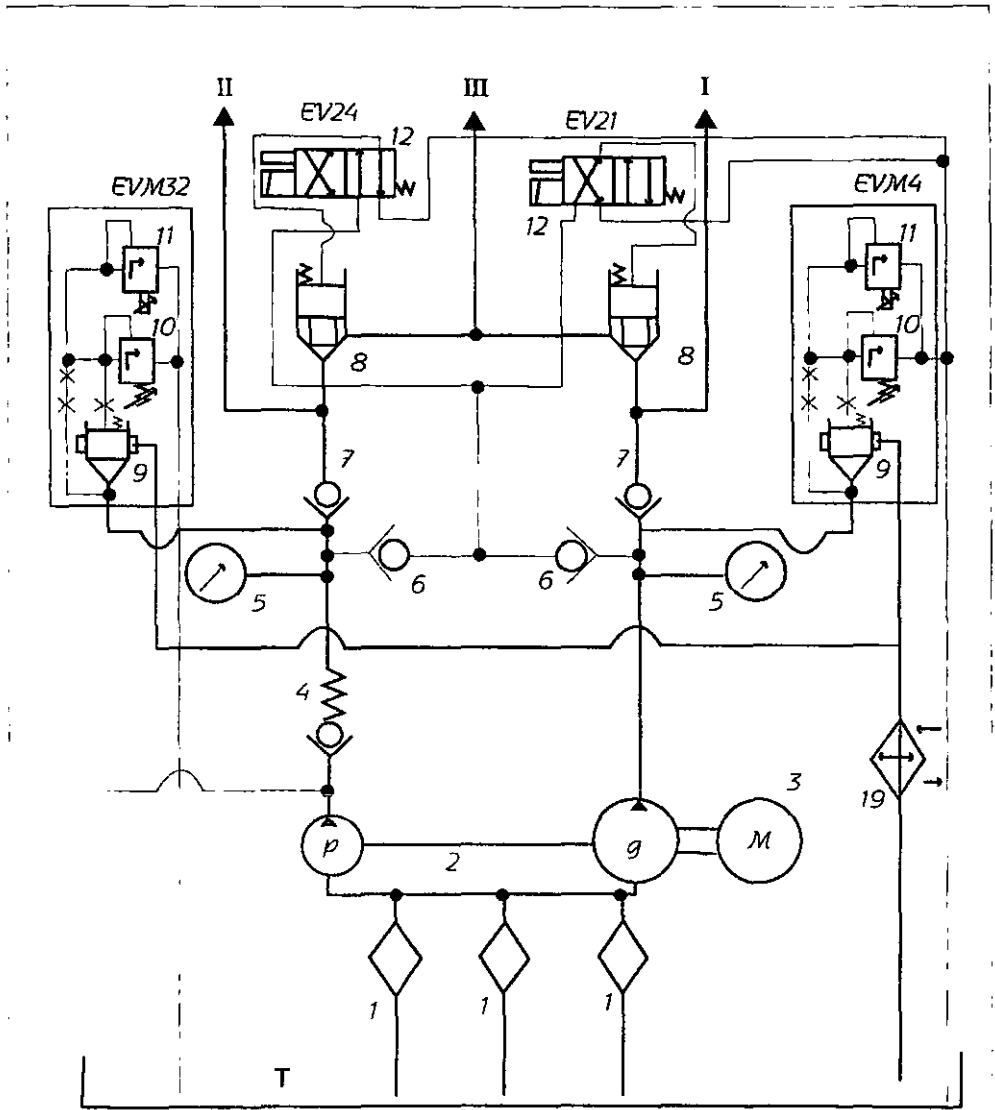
Grupo para el cierre de moldes por la bomba pequeña.
